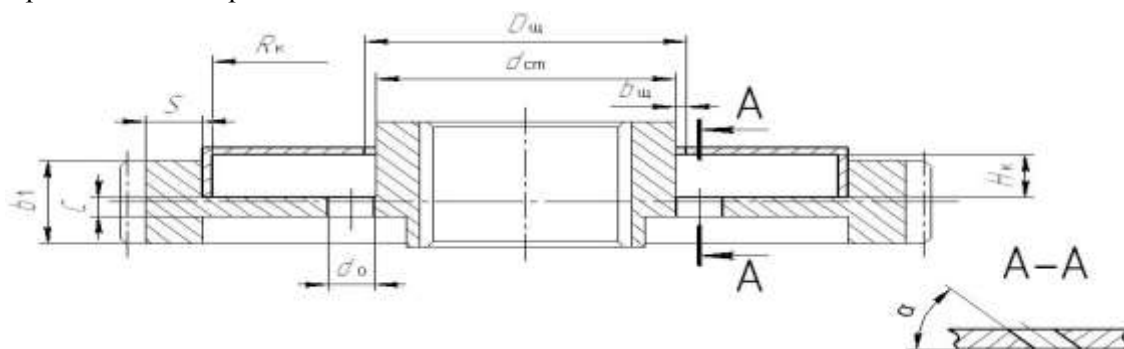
Схема конструктивных параметров шестерни, в полости которой закреплена цилиндрическая вставка
